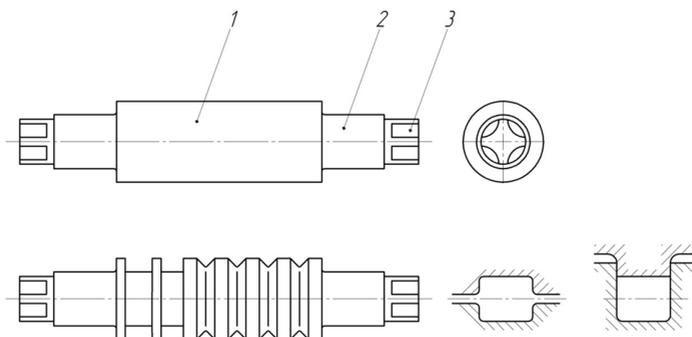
Инструмент для прокатки – гладкий и ручьевого валки:
